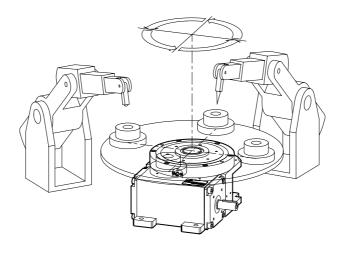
RIGIDIAL empleada como dispositivo de posicionamiento ante un robot de soldadura.
